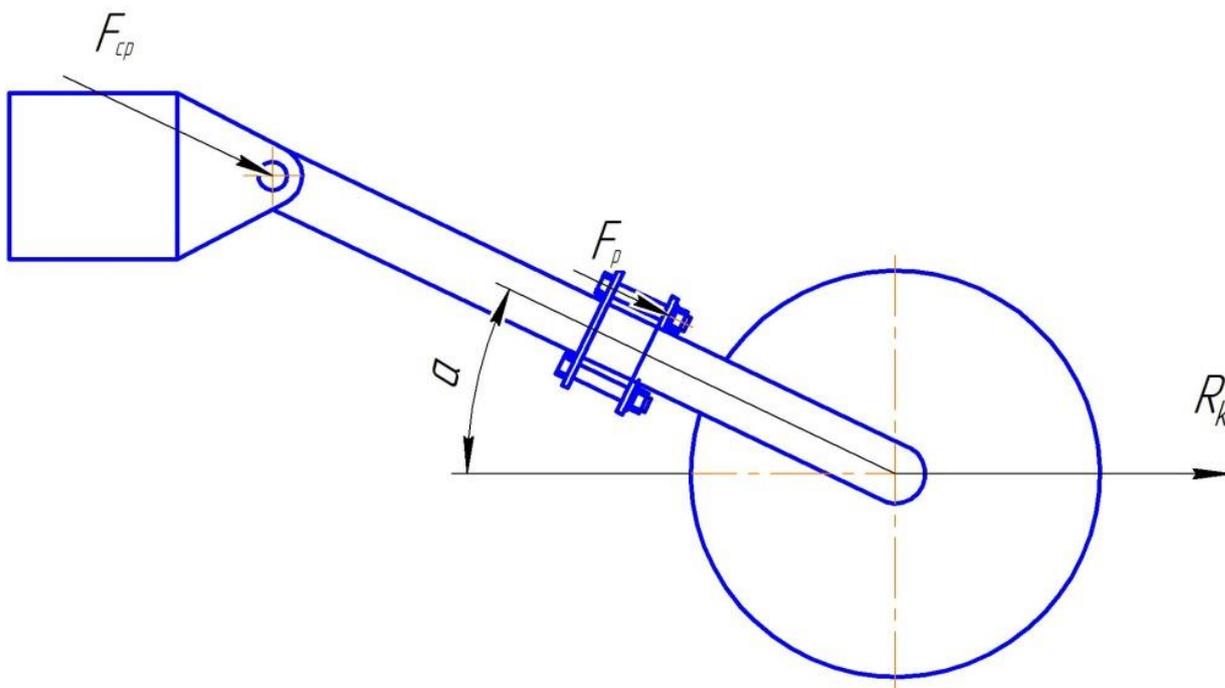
Схема для расчета соединений крепления зубового катка
